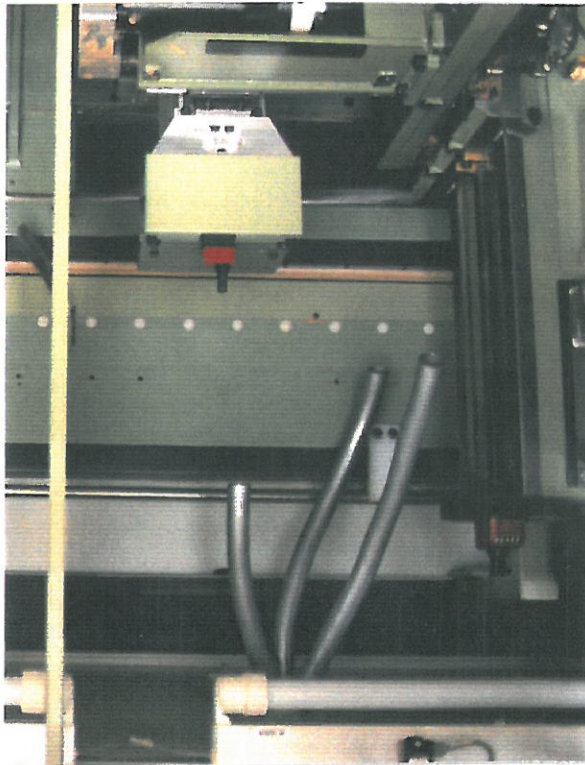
Spülluftzuführung für das erste Eckenfräsaggregat
